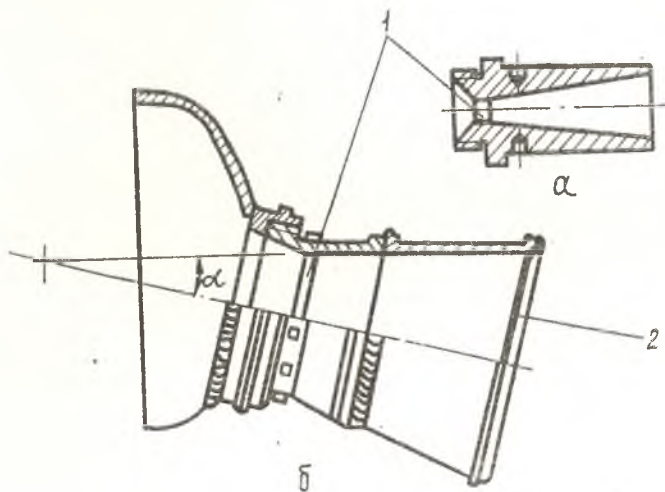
Простые сопла РДТТ: а — точеное; б — сварное, установленное под углом к оси двигателя: 1 — цилиндрическая проточка; 2 — заглушка
